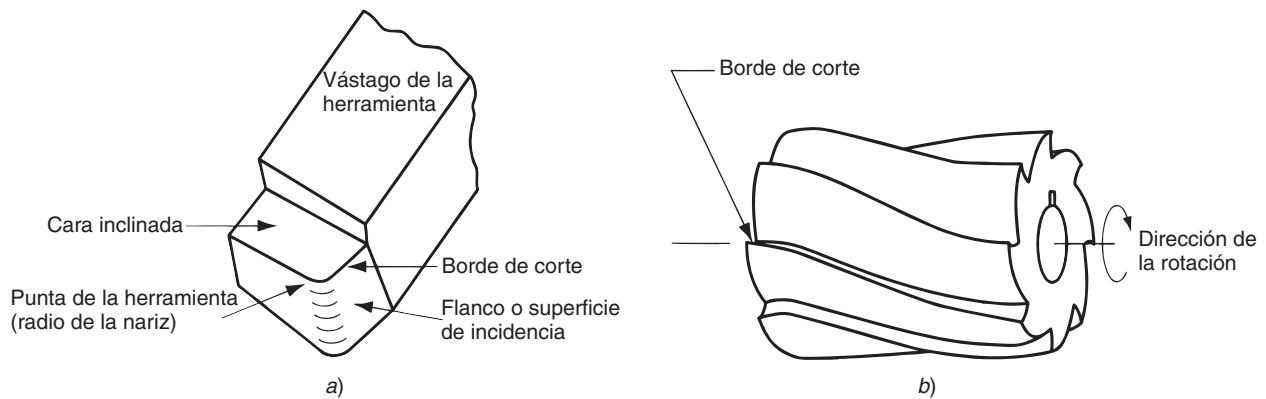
a) Una herramienta de una sola punta, que muestra la cara inclinada, el flanco y la punta, y b) una fresa helicoidal, representativa de las herramientas con bordes cortantes múltiples.
